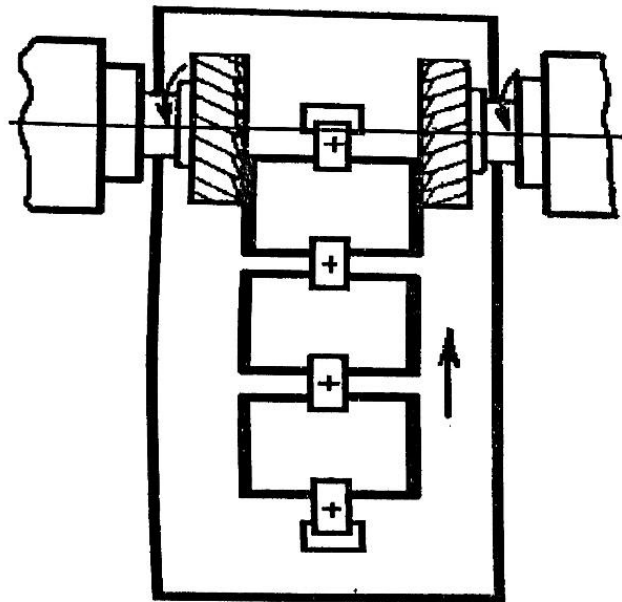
Обработка корпуса на продольно-фрезерном станке.
